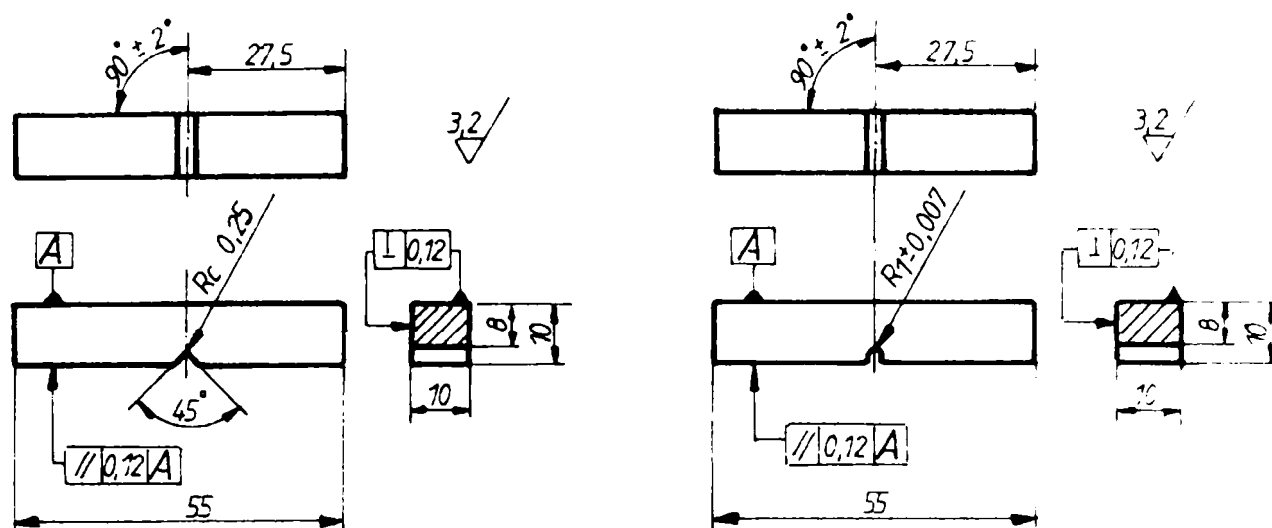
Forma și dimensiunile epruvetelor utilizate la încercări
